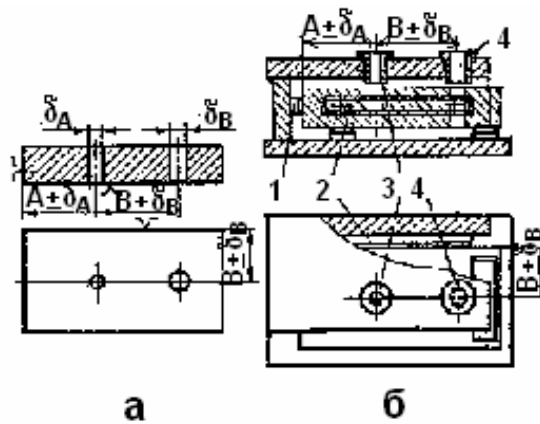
Схема виставлення розмірів і допусків на складальному кресленні кондуктора
